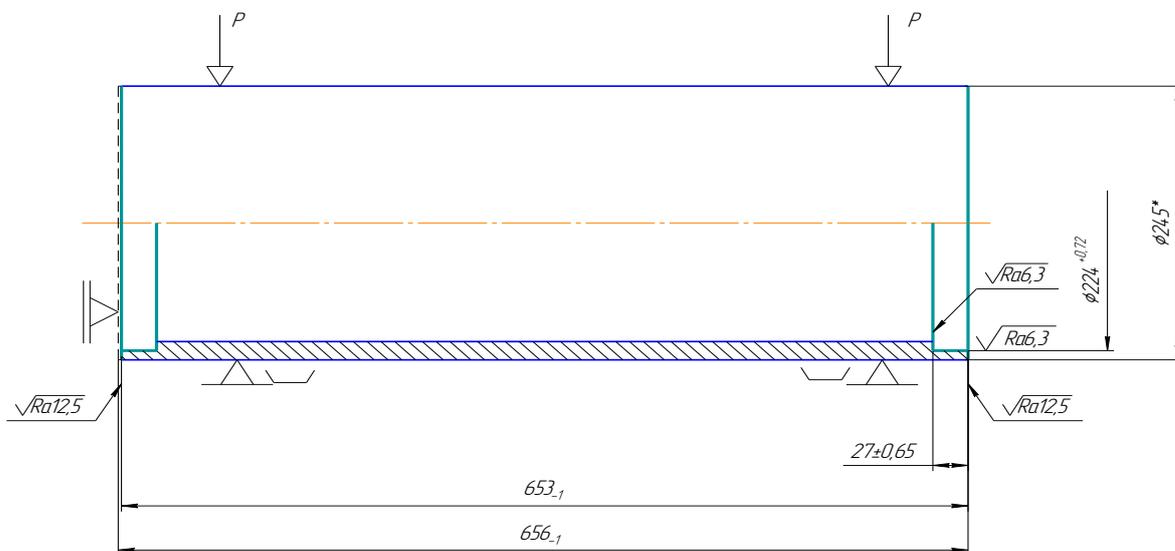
Схема установки для горизонтально-расточной операции 005
